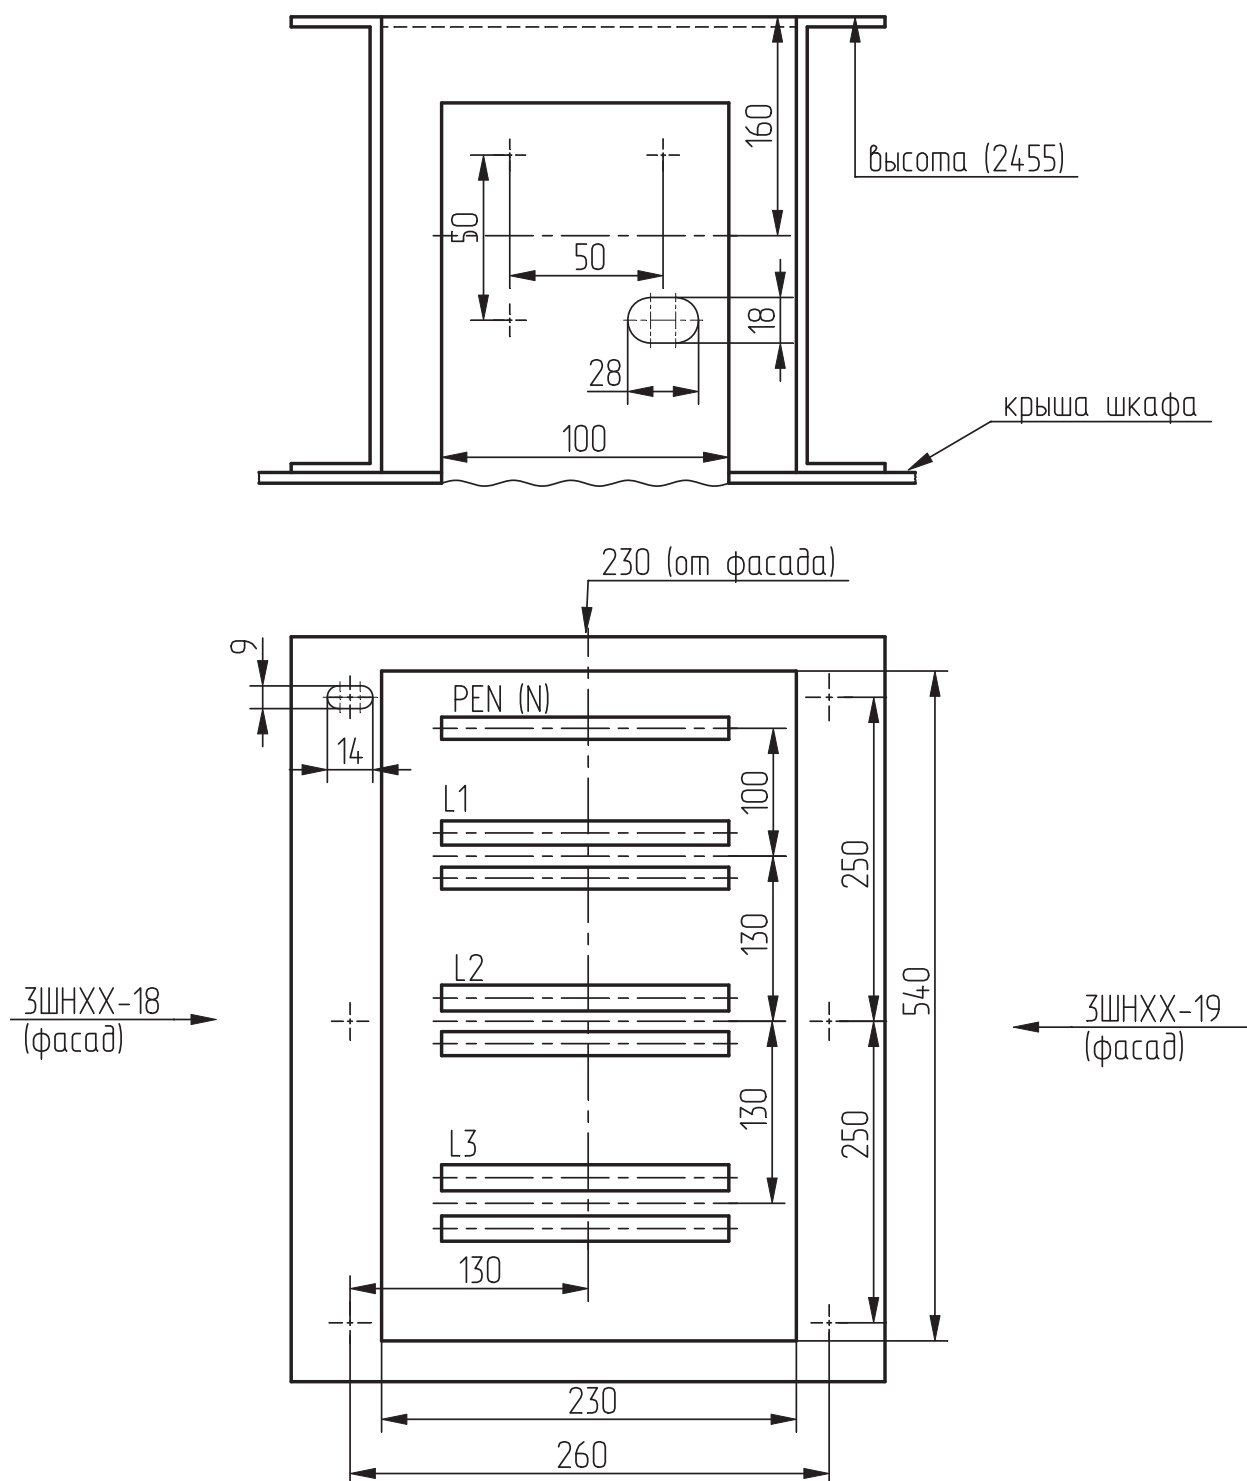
Присоединительные размеры для установки шинпровода на номинальный ток 2500 А
